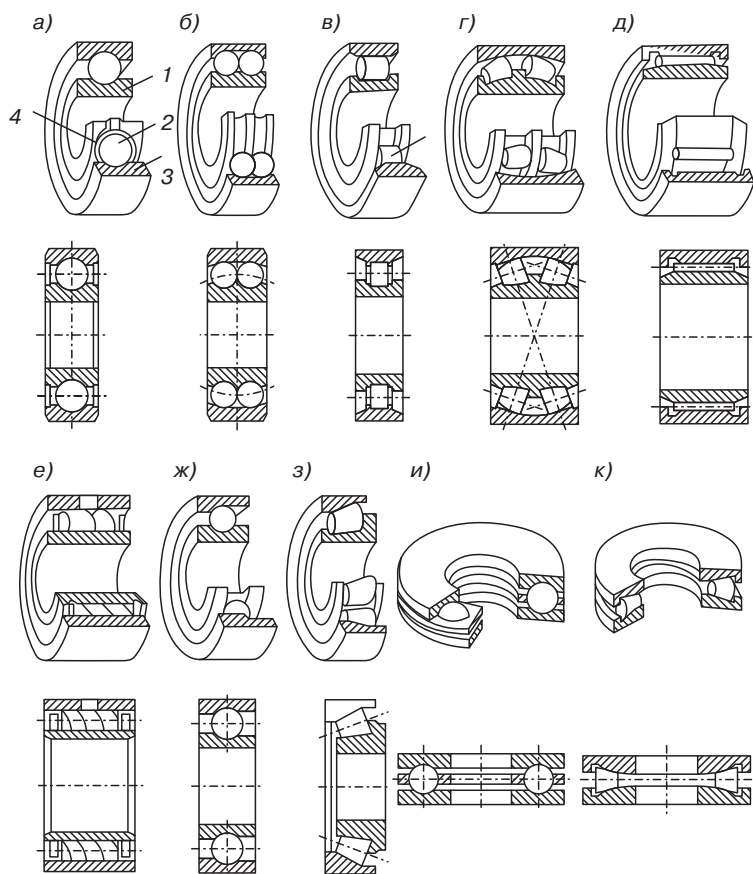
Основные конструкции подшипников качения: а — шариковый однорядный радиальный; б — шариковый двухрядный радиальный; в — роликовый однорядный радиальный с цилиндрическими роликами; г — роликовый двухрядный радиальный с бочкообразными роликами; д — роликовый радиальный с игольчатыми роликами; е — роликовый радиальный с витыми роликами; ж — шариковый радиально-упорный; з — роликовый радиально-упорный конический с коническими роликами; и — шариковый упорный; к — роликовый упорный с коническими роликами
